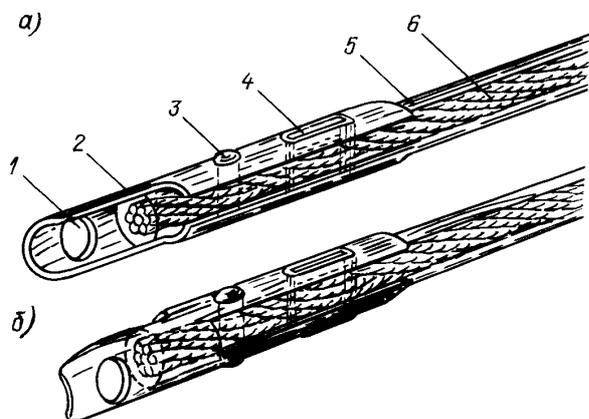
Образец наконечника (вид сбоку):
